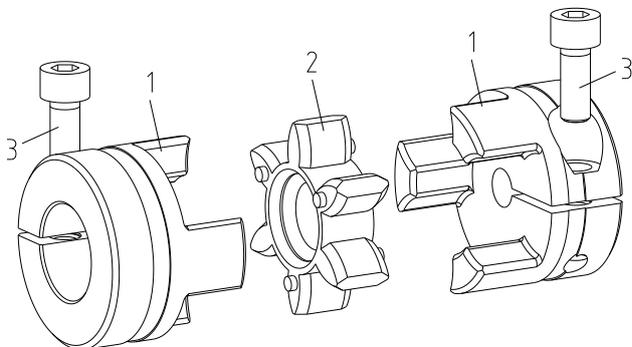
ROTEX® GS Compact (Gr. 7 - 19)
